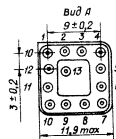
Габаритные размеры и цоколевка аналогового ключа в корпусе 2МС13-Г:
